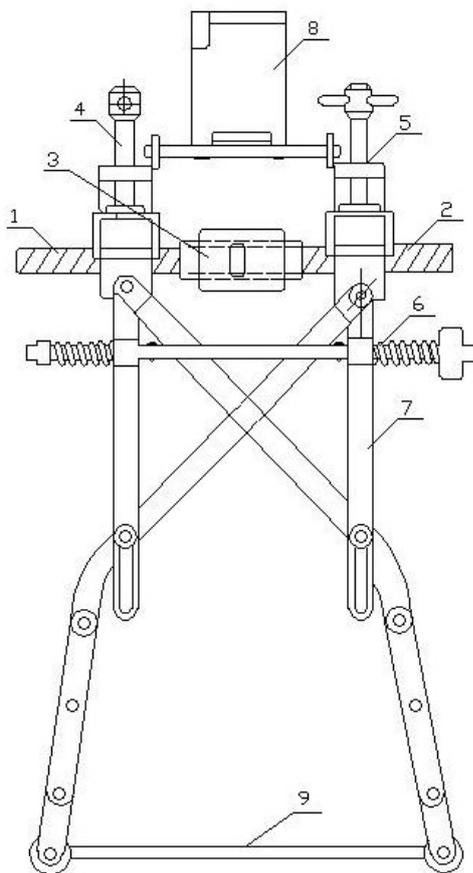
Клещи типов ПСП-2 и ПСП-3 для термитной сварки проводов:
